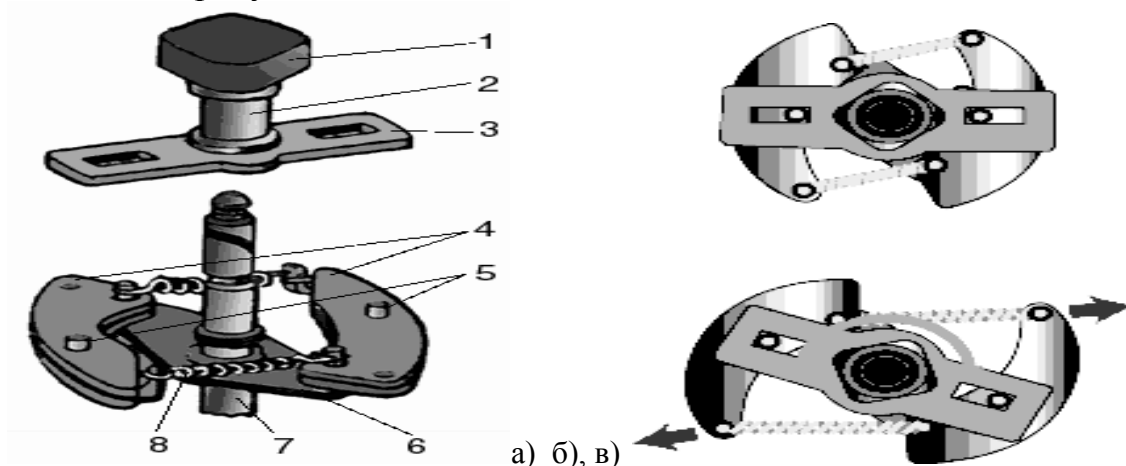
Схема работы центробежного регулятора угла опережения зажигания: 1 - кулачок прерывателя; 2 - втулка кулачков; 3 - подвижная пластина; 4 - грузики; 5 - шипы грузиков; 6 - опорная пластина; 7 - приводной валик; 8 - стяжные пружины. а) расположение деталей регулятора б) грузики вместе в) грузики разошлись
